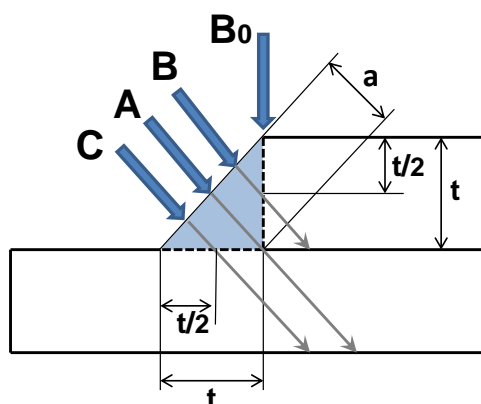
Posiciones del transductor sobre el cordón de soldadura para la inspección del mismo: *A*, en el medio del cordón; *B₀* en la intersección entre el material fundido y la chapa superior 1; *B* hacia la chapa superior 1 (derecha del cordón según la configuración representada) y *C* hacia la chapa inferior 2 (izquierda del cordón en la imagen). En las cuatro posiciones la dirección de penetración del ultrasonido dentro del material es perpendicular a la tangente de la cabeza del cordón en el punto de contacto.
